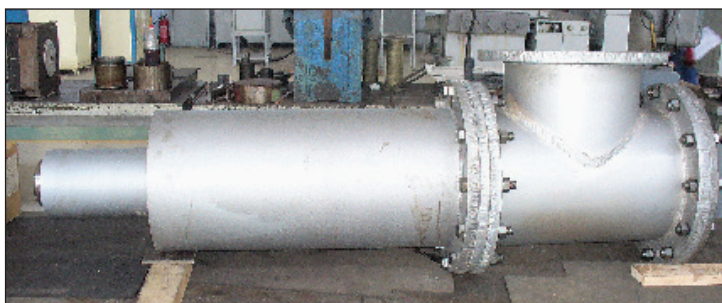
Общий вид модернизированной газовоздушной горелки ГНД-100 М для разогрева ковшей грузоподъемностью 60 и 90 т
